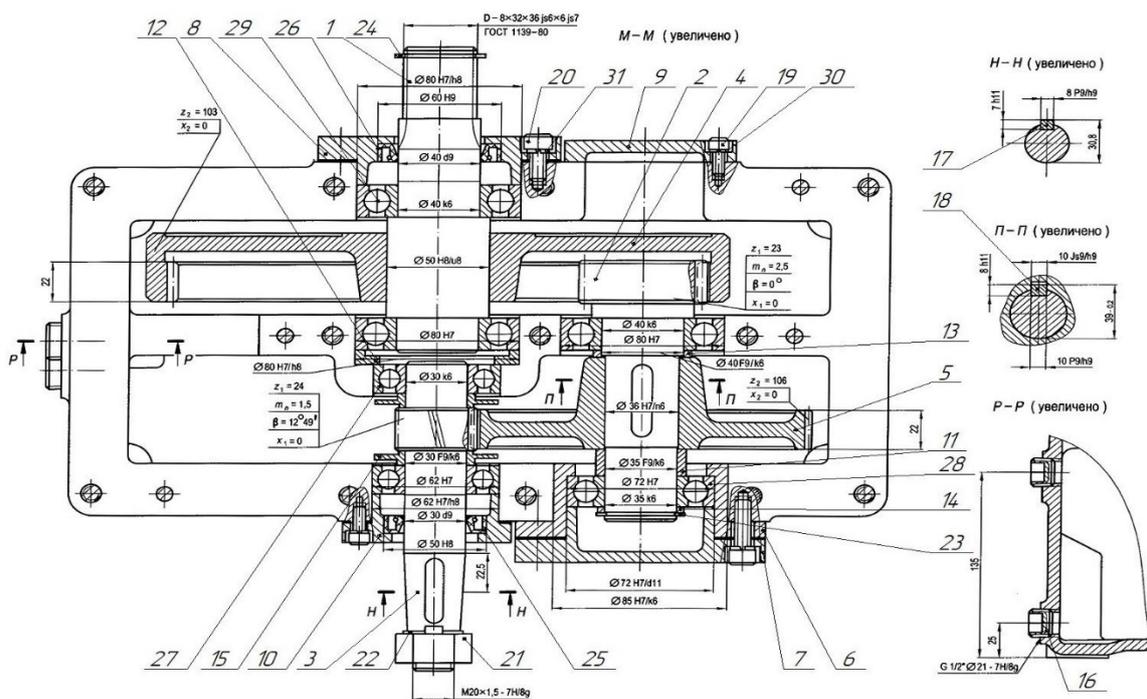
Двух ступенчатый цилиндрический редуктор с позициями деталей
